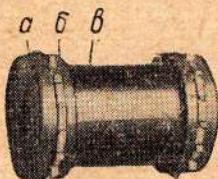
Скачковый барабан: а — шайба; б — зубчатый венчик; в — корпус барабана из пластмассы
